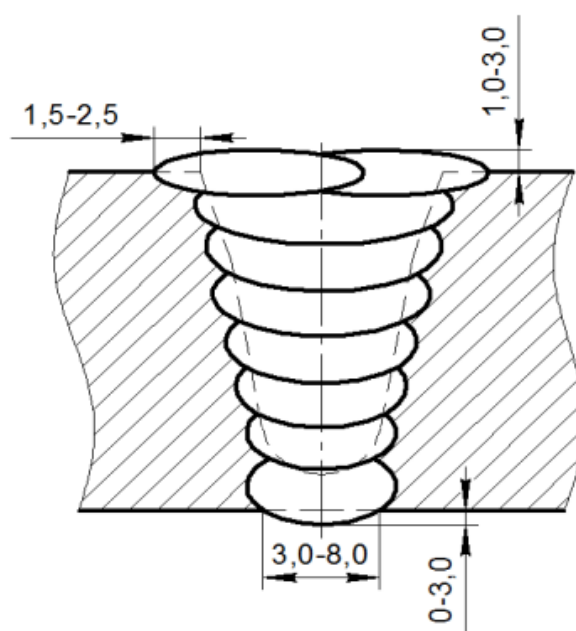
Форма и геометрические параметры сварного шва, выполненного проволокой сплошного сечения в среде активных газов смесях на медном подкладном кольце сварочными комплексами УАСТ-1
